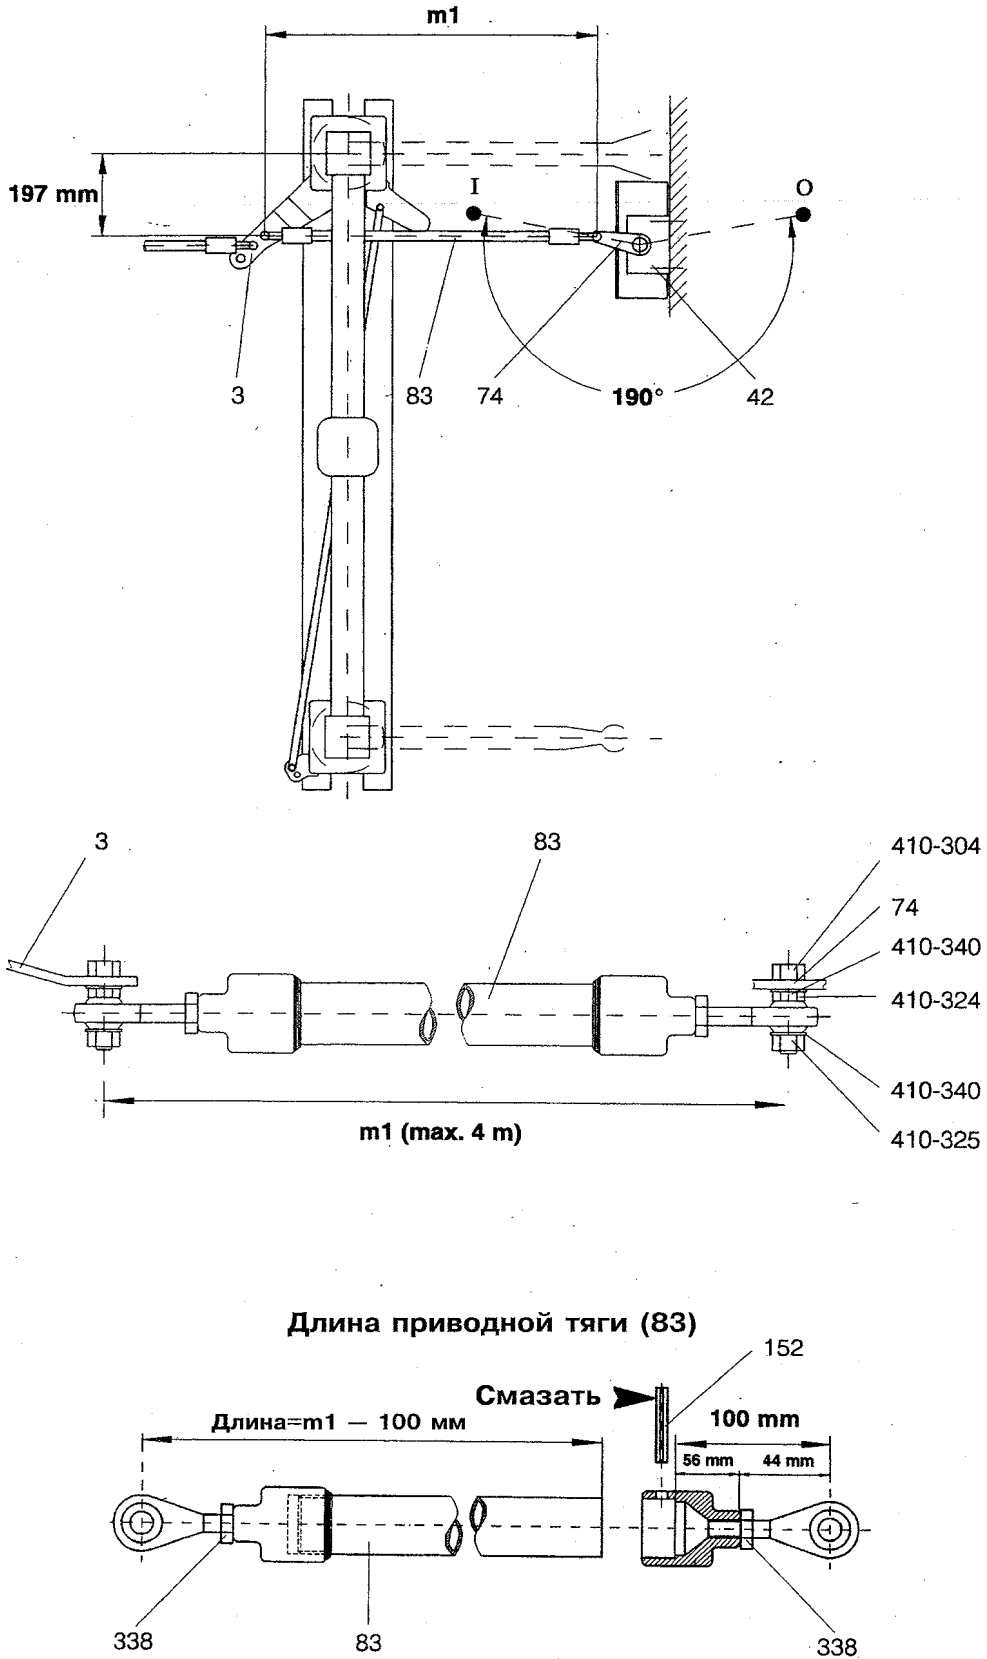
Установка приводного механизма разъединителя; раздельная установка: боковое смещение приводного механизма
